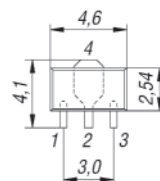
Pinbelegung und Abmessungen (SOT-89)
